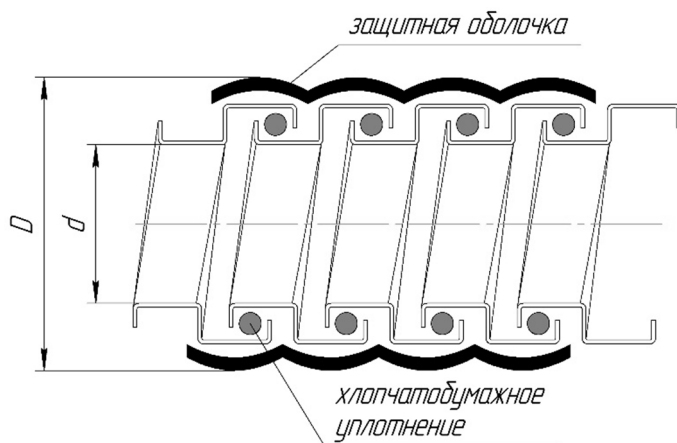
Конструкция герметичного металлорукава ГЕРДА-МГ
